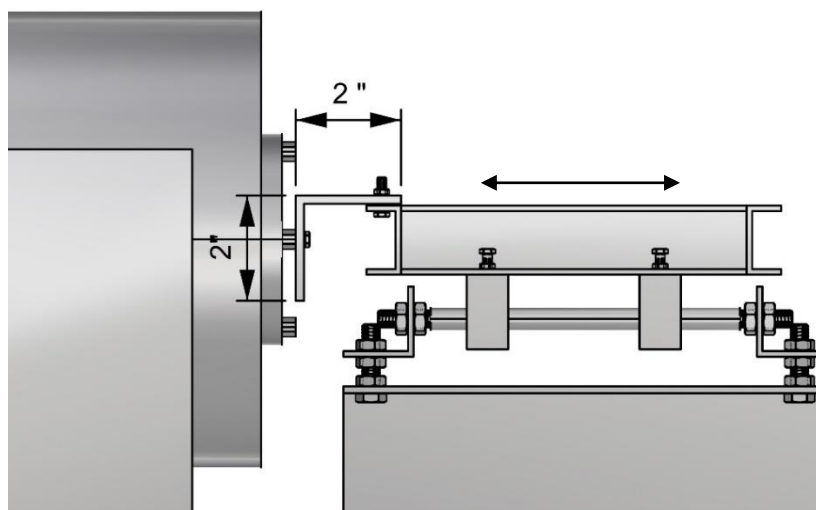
Perfil de conexión entre la armadura de agarre y el vibrador
